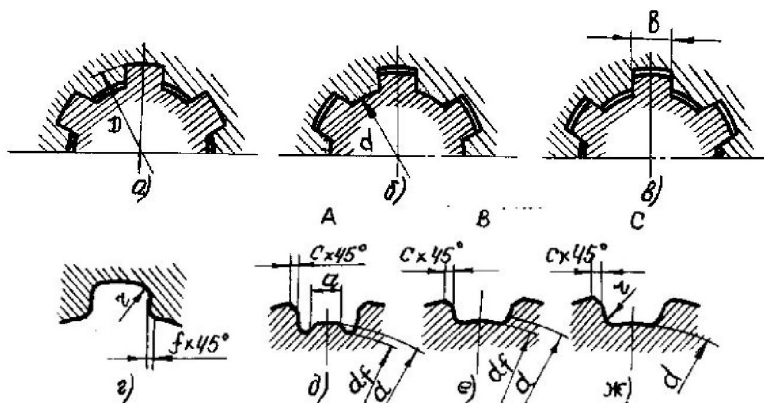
Виды центрирования прямобочных шлицевых соединений
